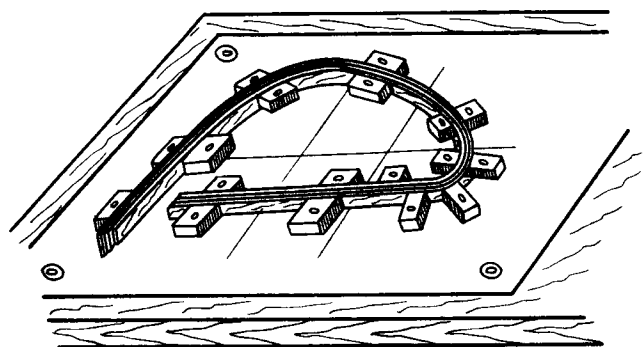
Изготовление закруглений из полосок шпона по чертежу
